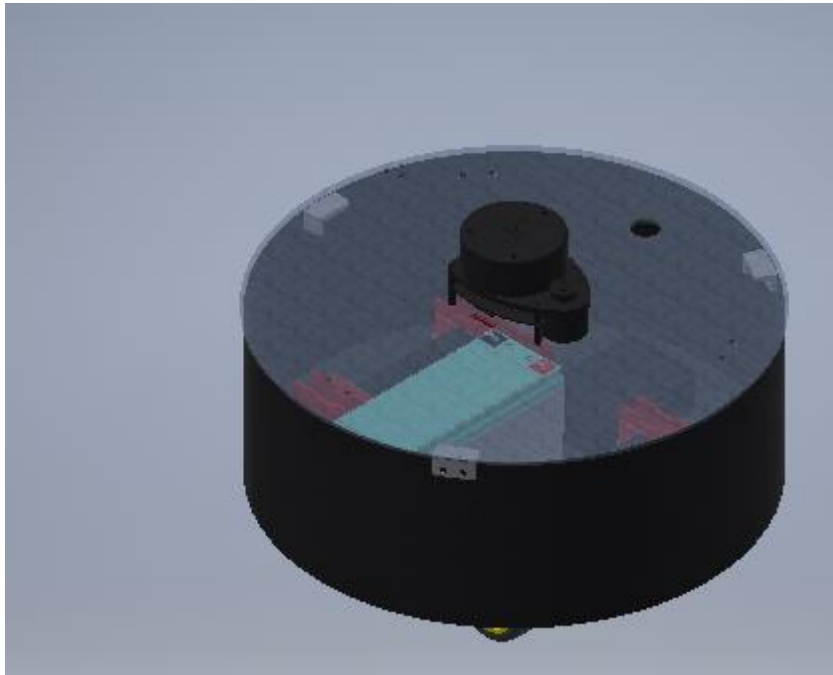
Robot ensamblado con Moduló de medición de Entorno
